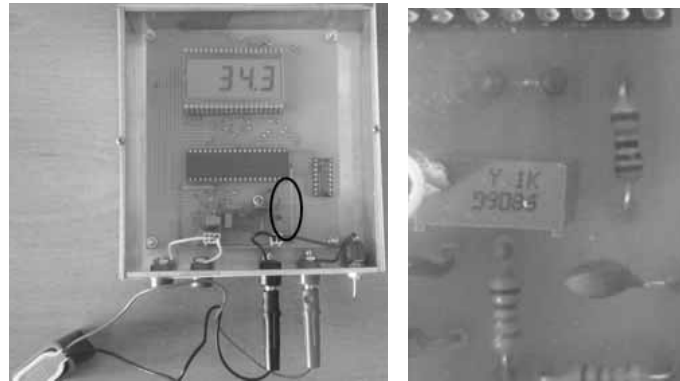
Placa PCB en la que se aprecian los componentes soldados.
